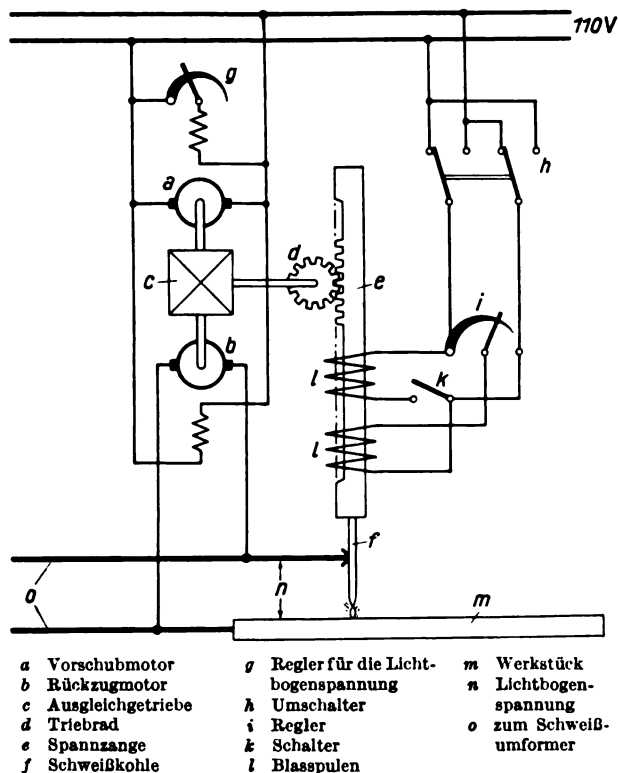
Schaltanordnung des Schweißautomaten mit relaisloser Steuerung.
